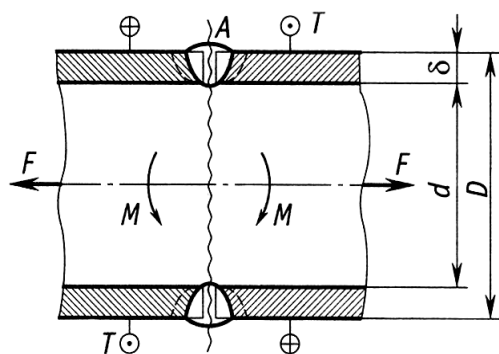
Расчетная схема сварного соединения стыковыми швами
